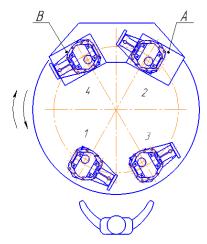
Сборочный установка с поворотным столом "Gehomat"
